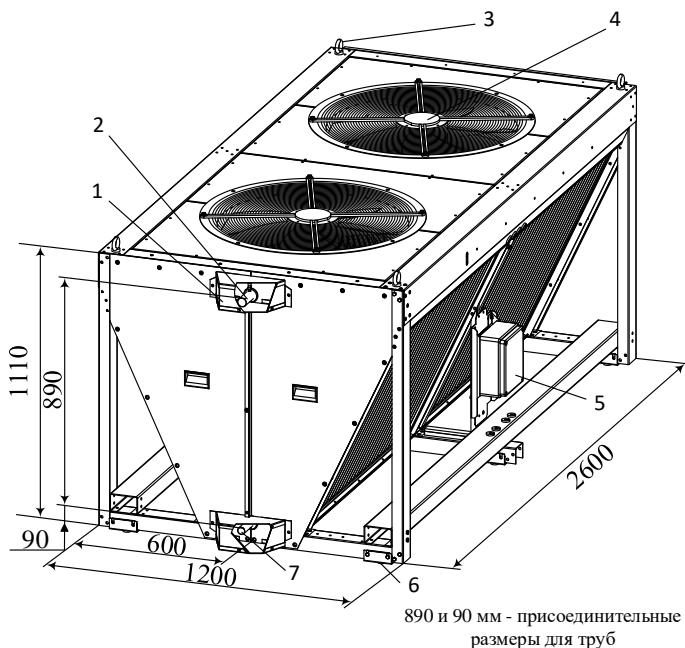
Компоновка и основные размеры конденсаторов 163 и 190
